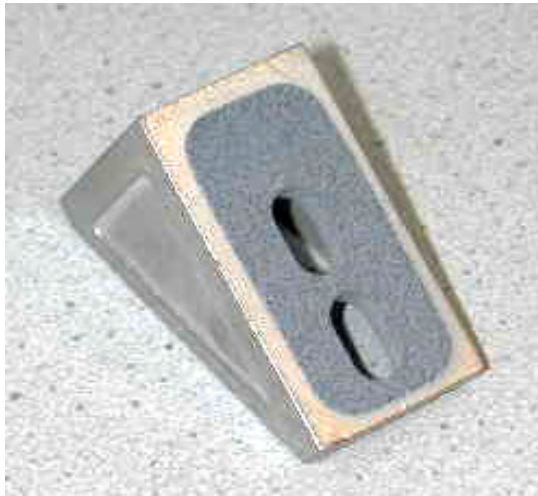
Keramikbeschichtetes Bauteil mit griffiger Oberfläche
